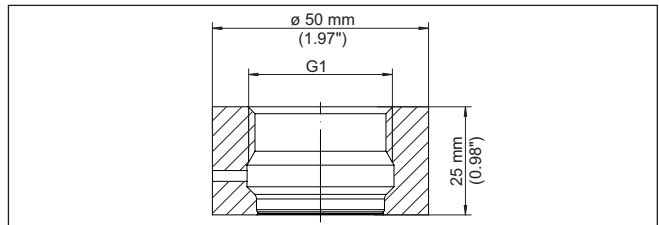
Maße Einschweißstutzen G1 (ISO 228-1) - O-Ring-Dichtung
